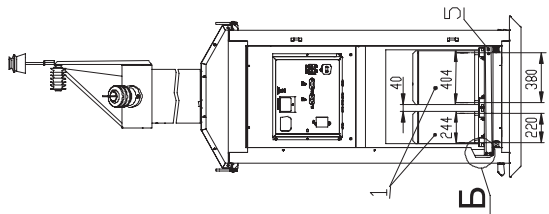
Общий вид сверху с двумя БДР (вариант К.11)
